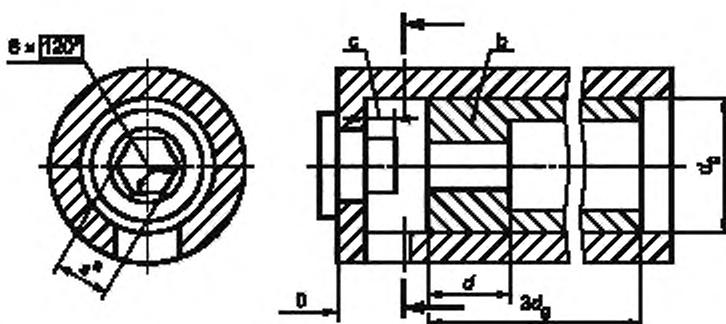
Калибр для проверки допуска формы, установленного на рисунках 24 и 72.
